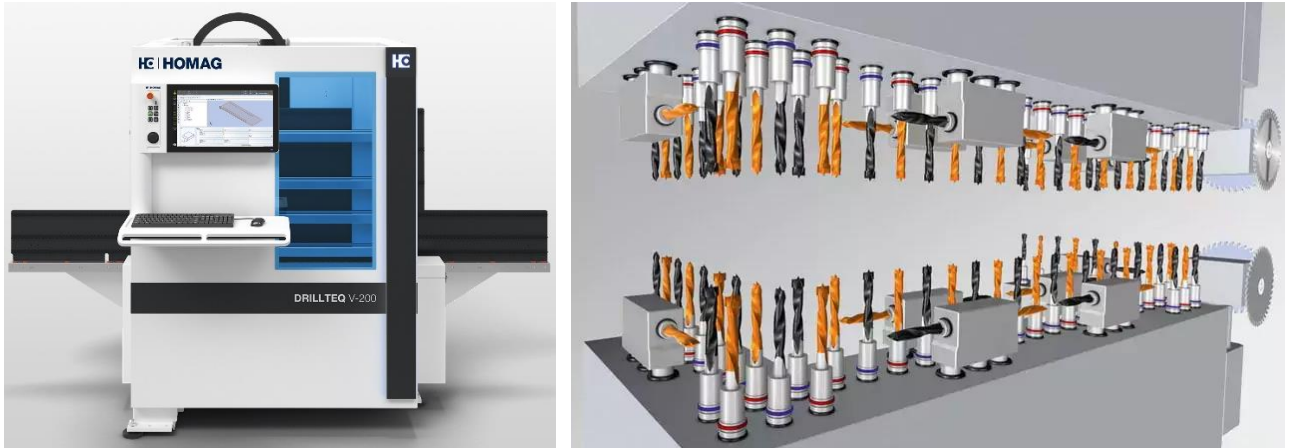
Вертикальний свердильно-присаджувальний центр з ЧПК моделі DRILLTEQ V-200 та його магазин інструментів
